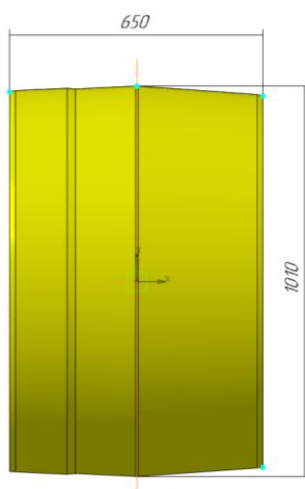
Бочка прошивного стана ТПА 220 после реконструкции. 3D модель
